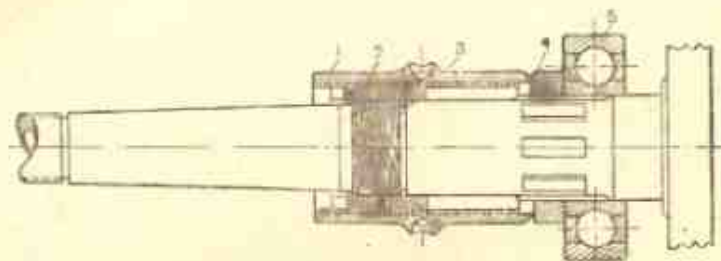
Приспособление для посадки переднего опорного подшипника:
